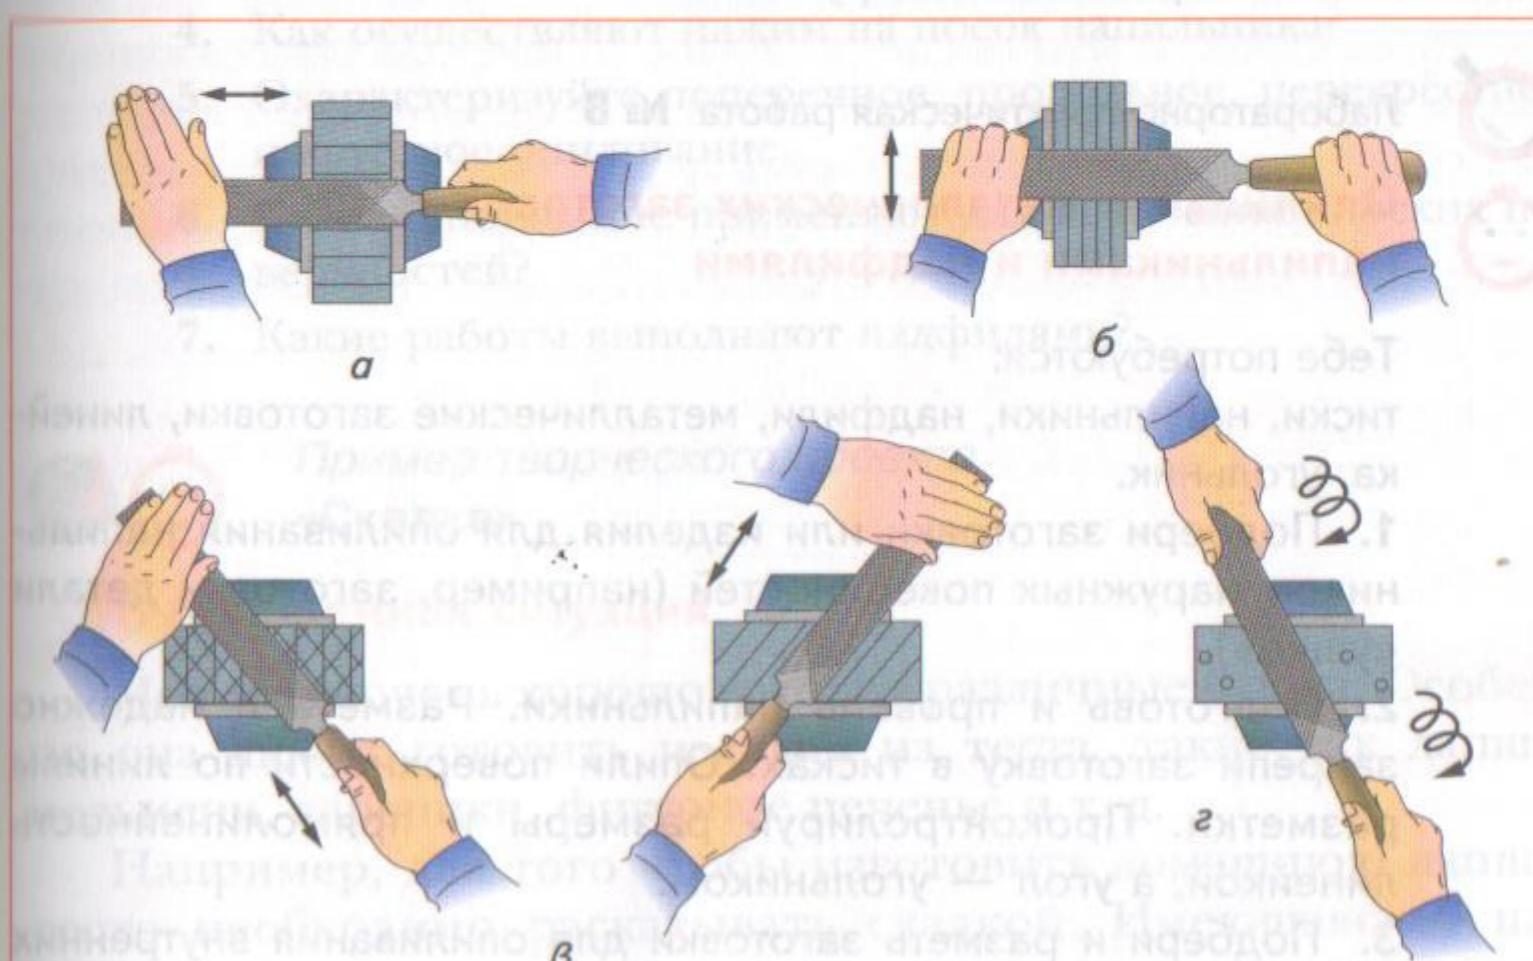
Приёмы опиливания напильником: а — продольное; б — поперечное; в — перекрёстное; г — круговое
